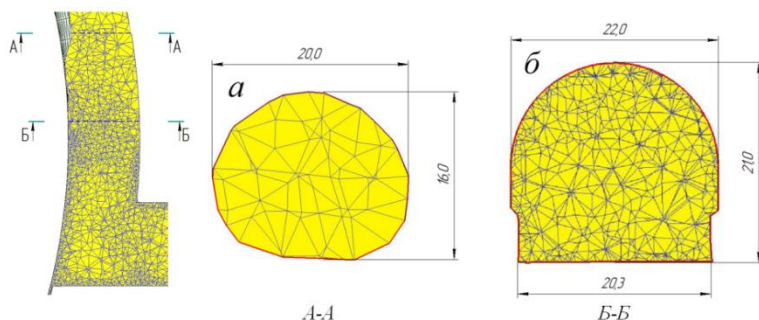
Распрессовка заготовки перед переходом в форкамеру:
